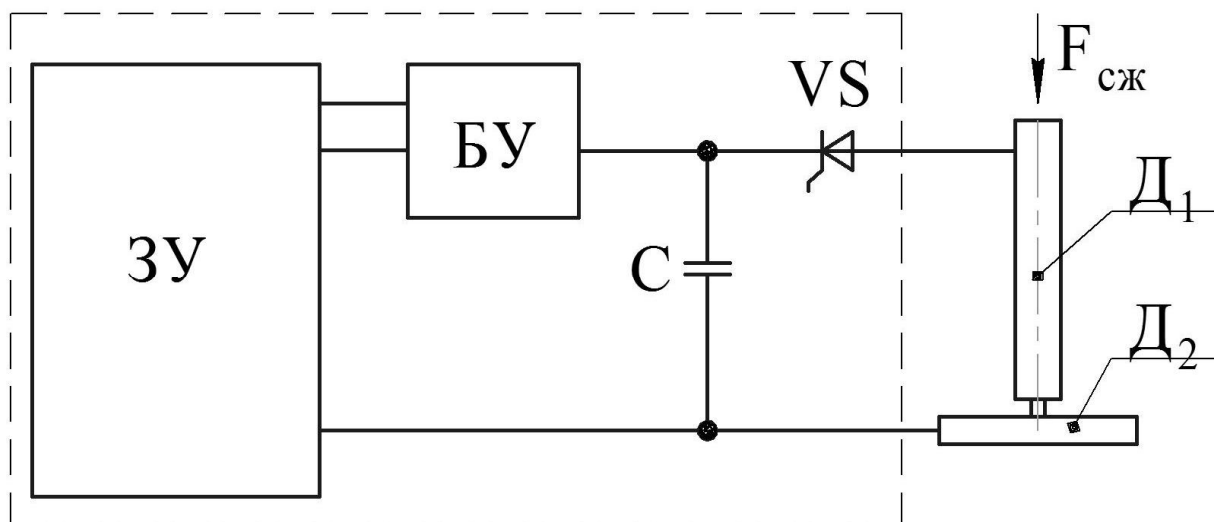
Принципиальная схема CD Stud Welding
